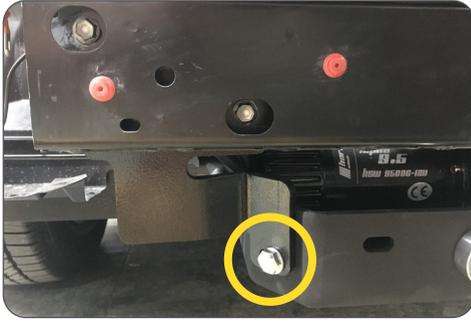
Befestigung Versteifung mit Windenplatte links / mounting stiffener, left side
